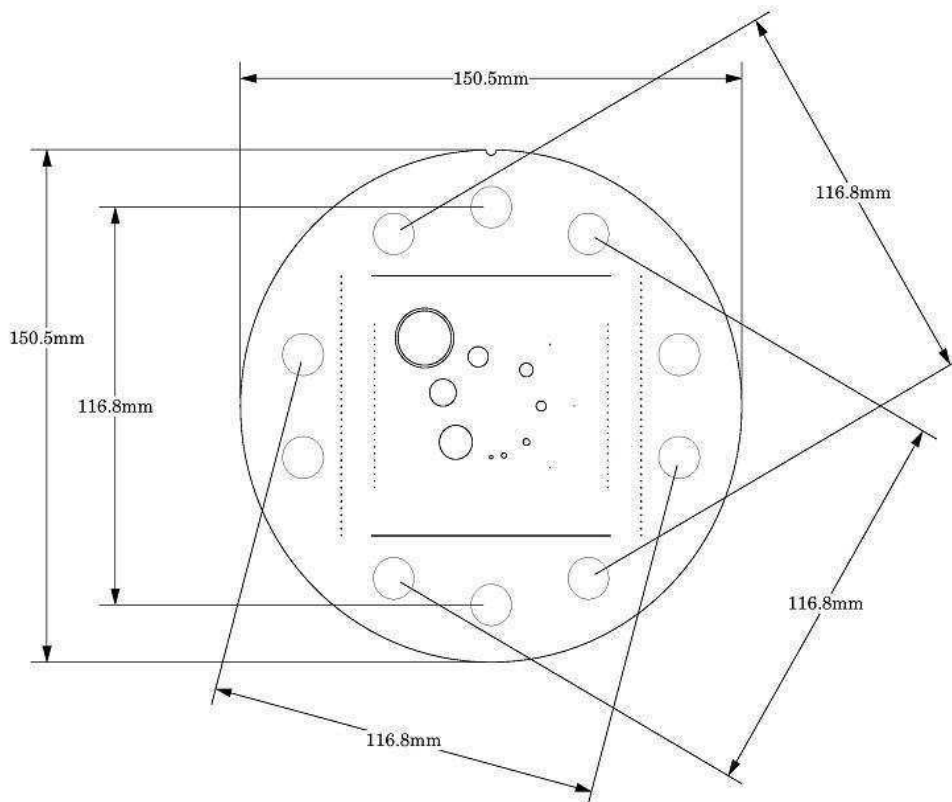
Módulo CTP 682. Dimensiones acotadas entre diferentes componentes del módulo.
